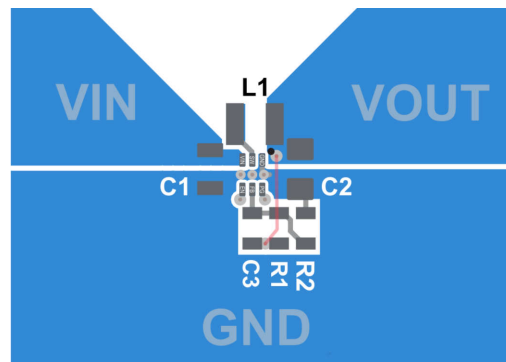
TPS62A0x (SOT563) PCB Layout Recommendation
